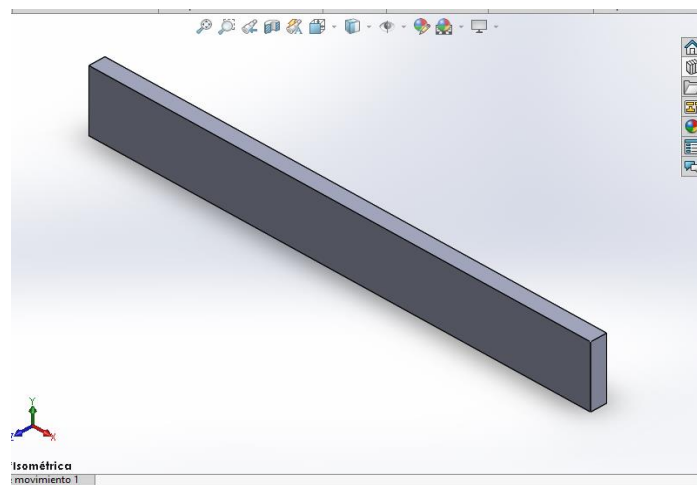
Diseño CAD de probeta para ensayo de flexión.
